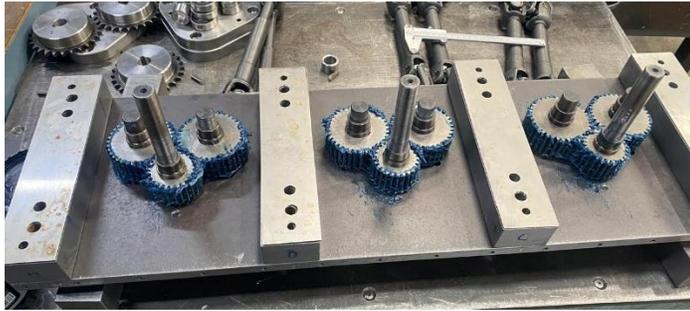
Montaje de caja de engranajes. Fuente: Autor.
